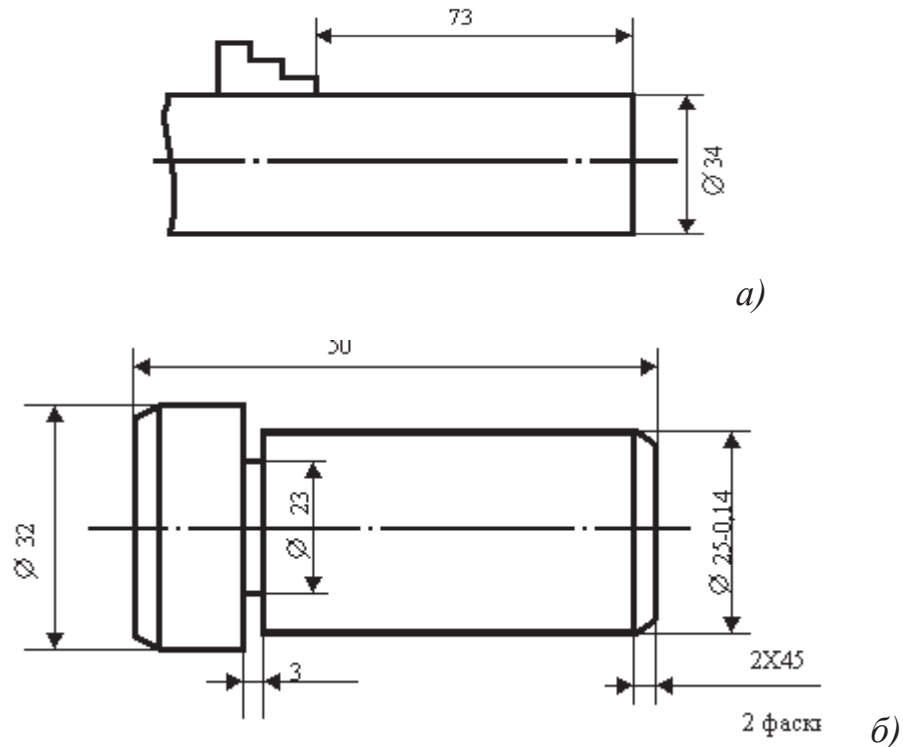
Заготовка для деталі „палець» (а) і готова деталь (б).
